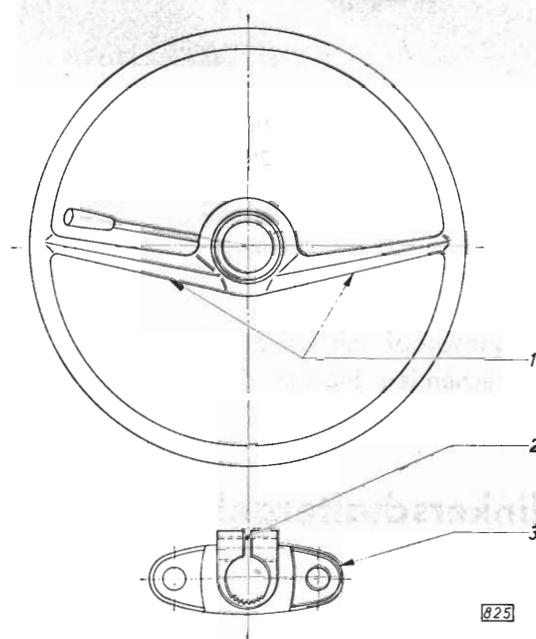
Lenkrad zum Lenkspindel flansch ausrichten
